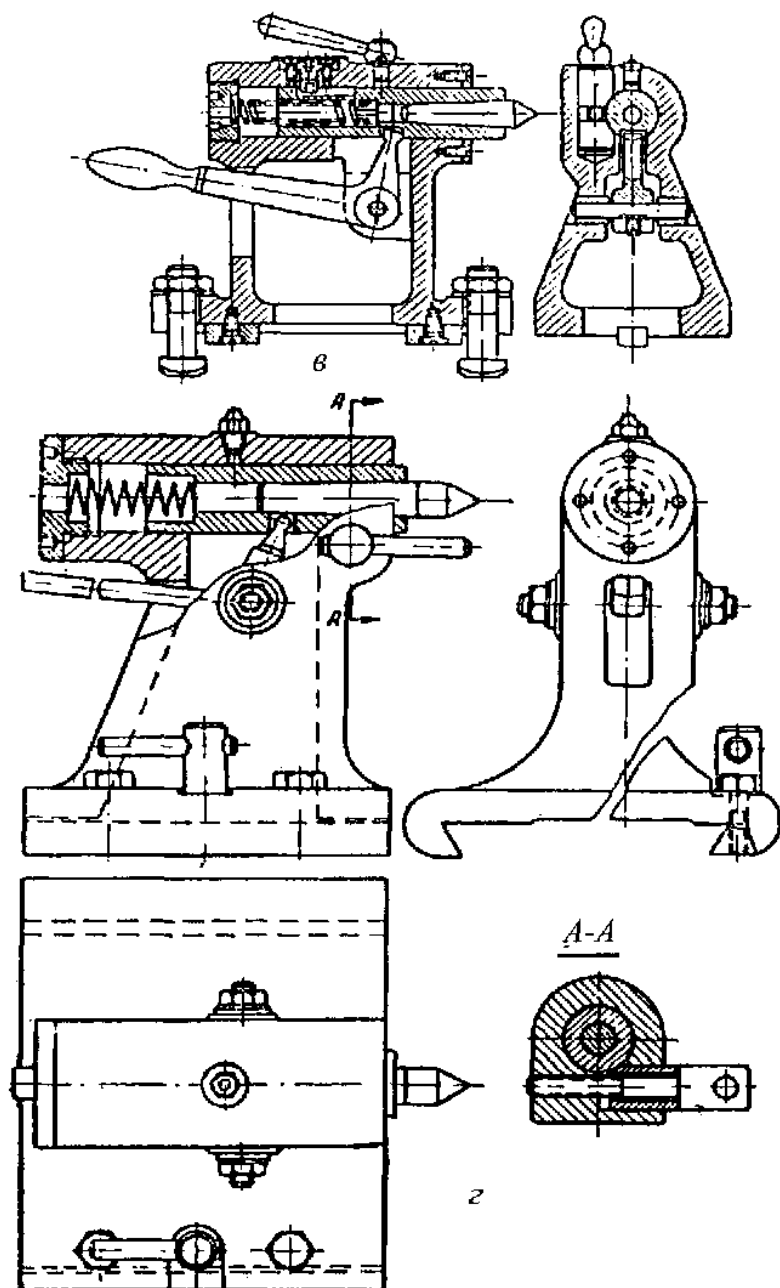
Бабки з рухомим центром: б, з – центр змінний з жорсткою пружиною для базування важких деталей;
